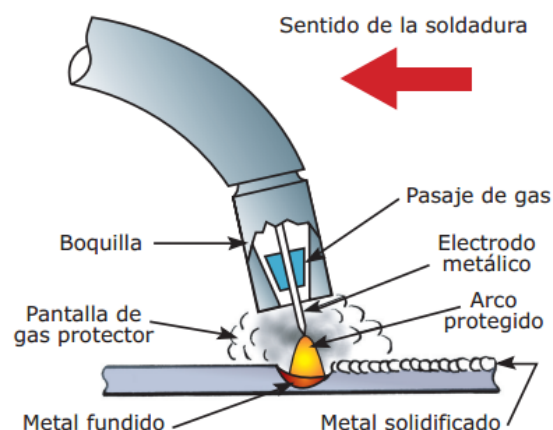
Efectos producidos en una soldadura MIG
